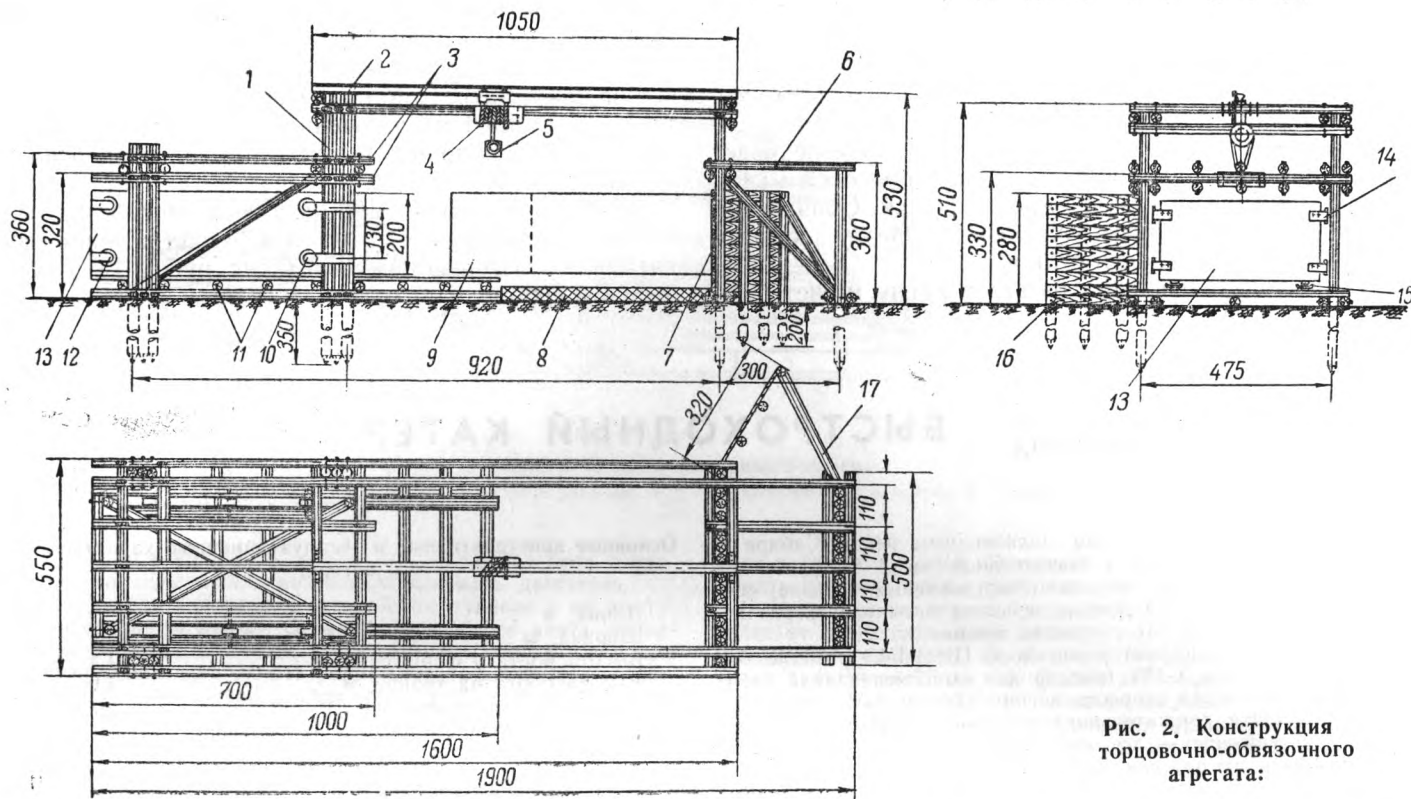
Конструкция торцовочно-обвязочного агрегата:
